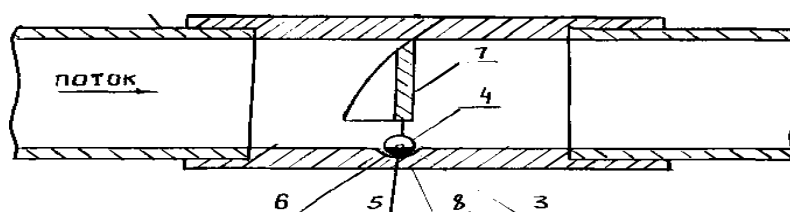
Схема устройства для выравнивания напора по длине внутрипочвенного увлажнителя: 1 - трубчатый увлажнитель; 2- корпус; 3 - углубление; 4- шаровой противовес; 5 - свинец; 6 - отверстие; 7 - клапан; 8-ось противовеса.
